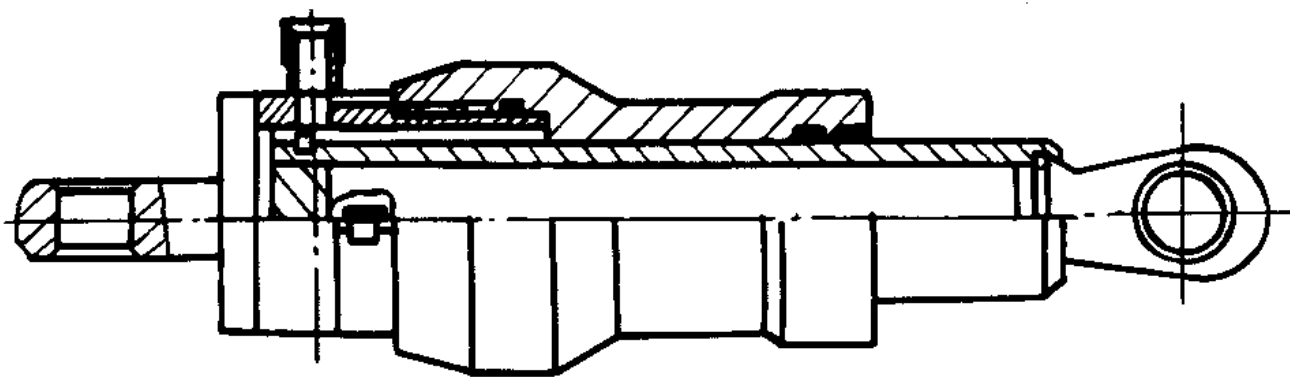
Гидроцилиндр наклона силосопровода Н20.10.000-07.
